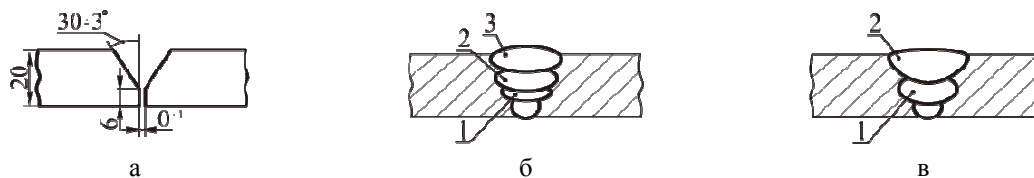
Конструктивные элементы подготовленных кромок (а) и схематическое изображение сварного соединения, выполненного без воздействия ПОМП (б) и с воздействием ПОМП (в)
